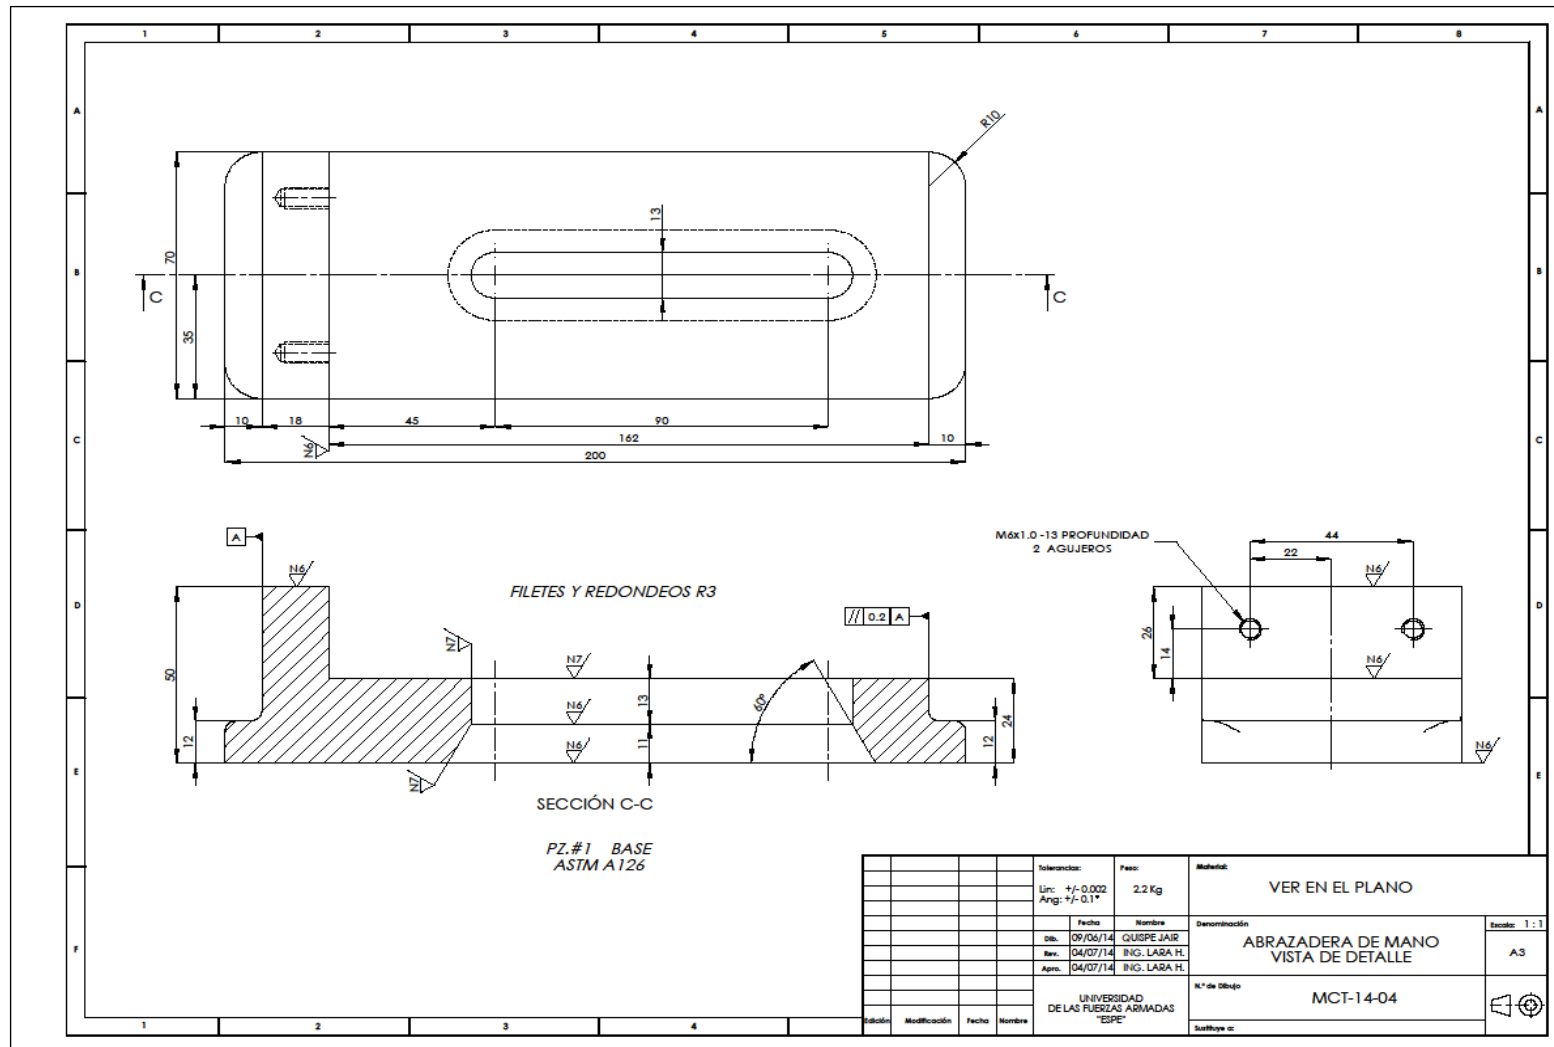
Ejemplo 1 de un plano de detalle.
